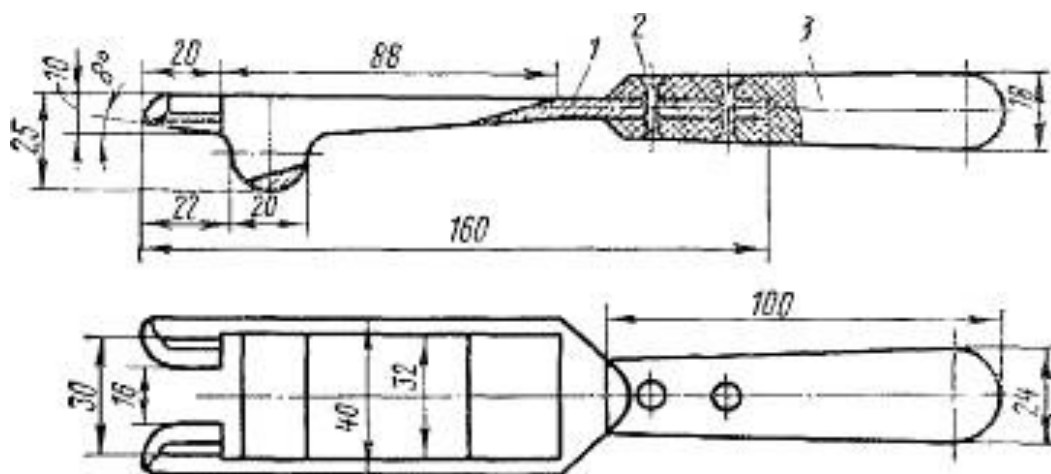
Рычаг для отжатия пружин толкателей плунжеров:
